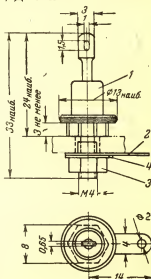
Габаритный чертеж диодов Д815А—Д817ГП.
